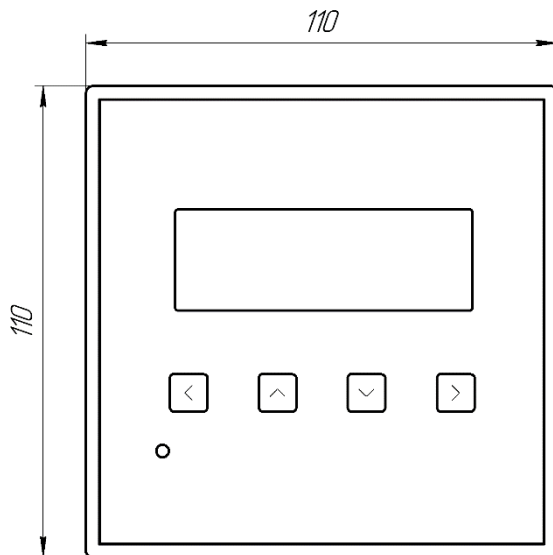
Габаритный чертеж счетчика SM-хАС (вид спереди)
